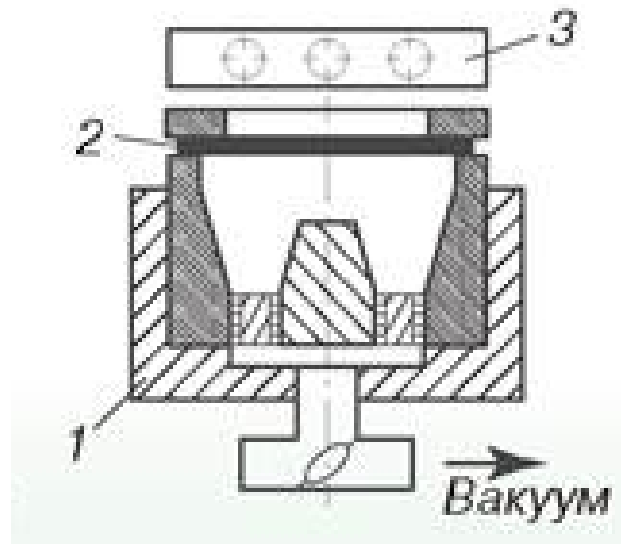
Схема процесу вакуумної формовки: 1 – герметичний корпус, приєднаний до вакуумного насосу; 2 – листовий термопластичний матеріал; 3 – нагрівальний елемент [26].
